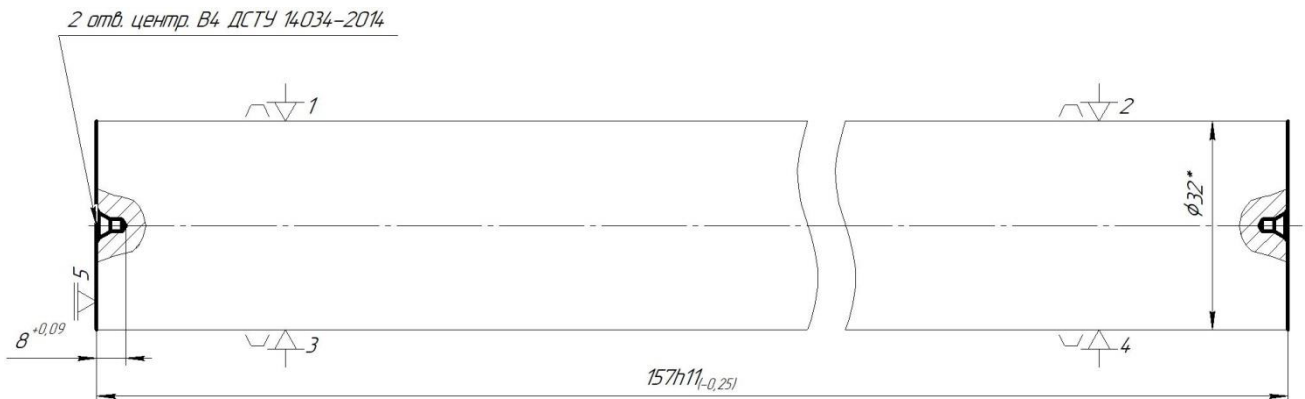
Схема установки заготовки в самоцентрувальні призми
